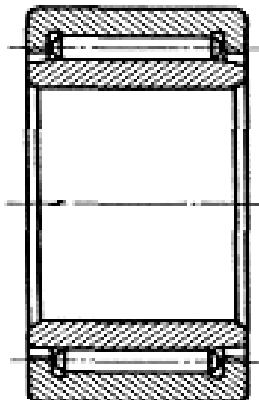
Роликовый радиальный подшипник с игольчатыми роликами
